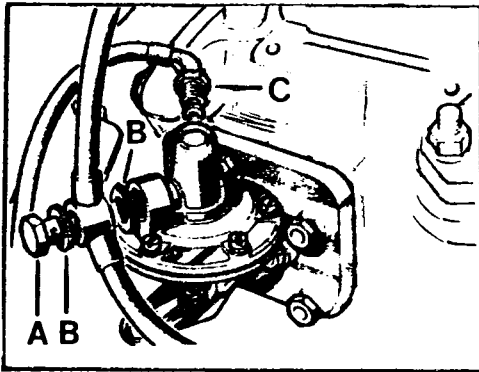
Desmontaje tuberías bomba - de combustible
